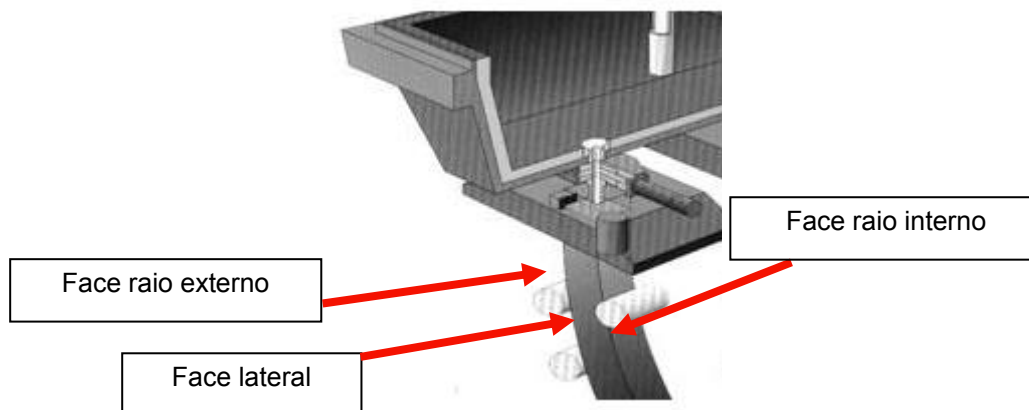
Desenho representativo da máquina de lingotamento contínuo, mostrando as faces do molde.
